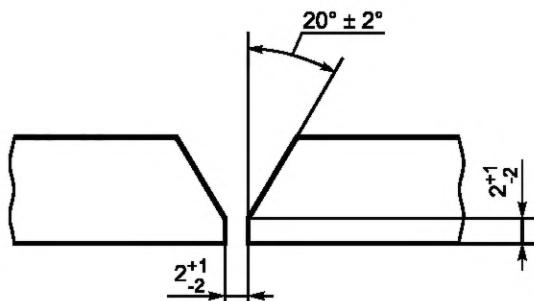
Конструктивные элементы подготовки кромок под сварку
